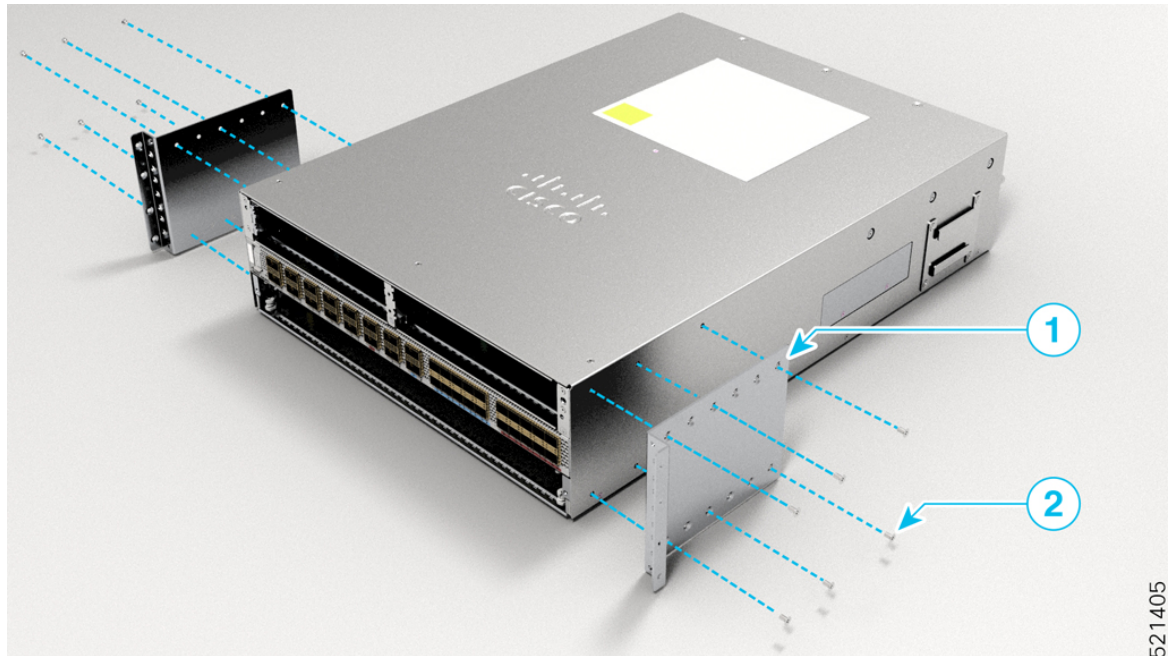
Cisco ASR 9902: Montageklammern für 23-Zoll-Rack mit vier Säulen an den Seiten des Chassis befestigen
